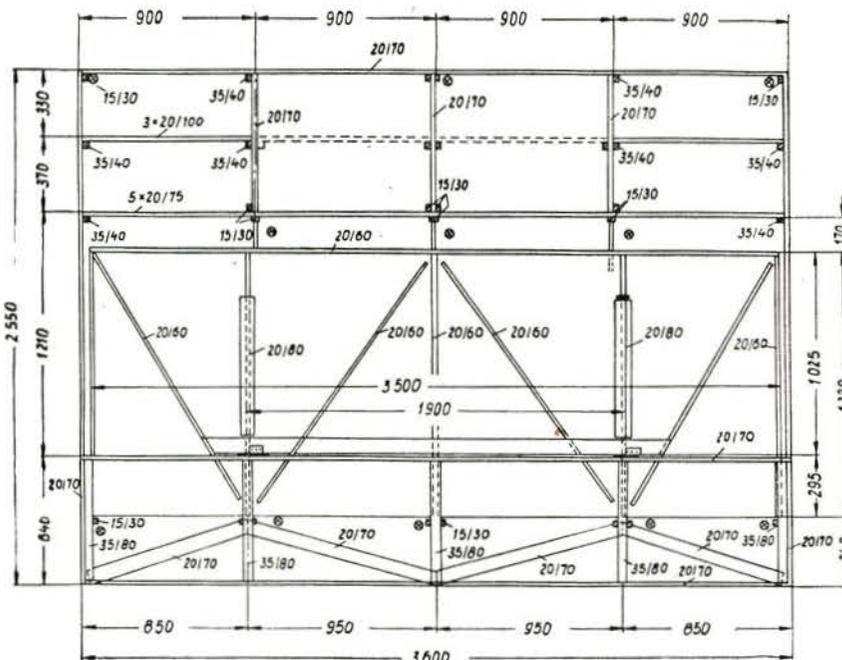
Draufsicht auf Konstruktion des Klappschranks einschließlich eingehängter Grundplatte
